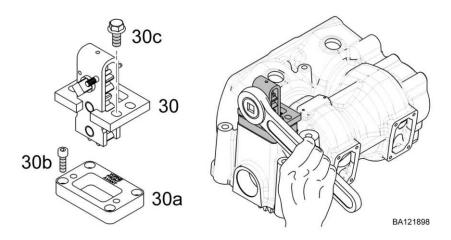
Dispositivo de giro — Montaje compresor, herramienta especial nº. 30 hasta 30c
